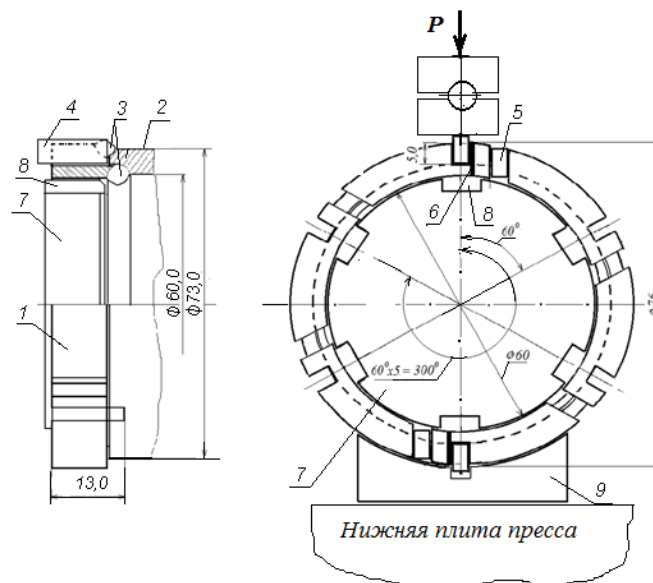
Общий вид коронки для испытания крепления резцов на прочность:
